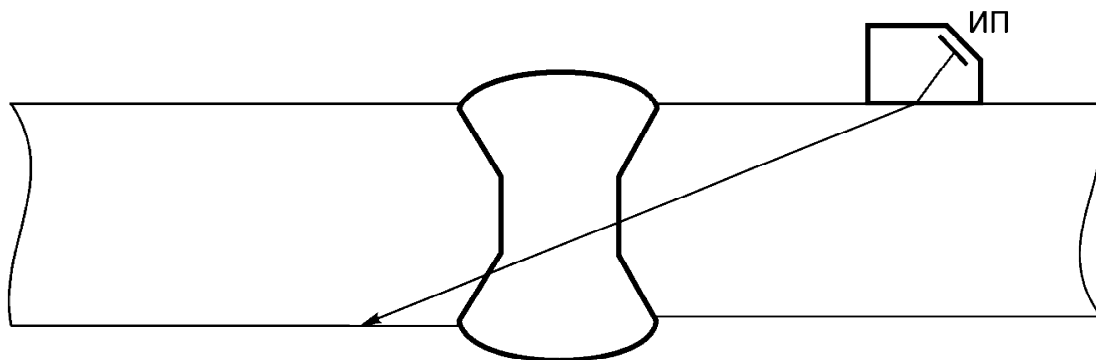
Схема прозвучивания стыкового сварного соединения прямым лучом
